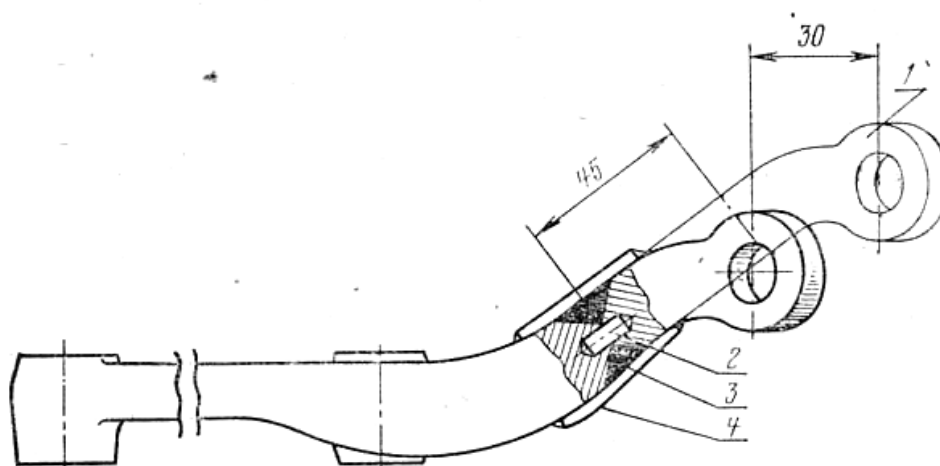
Переделка поворотного рычага автомобиля М-412:
